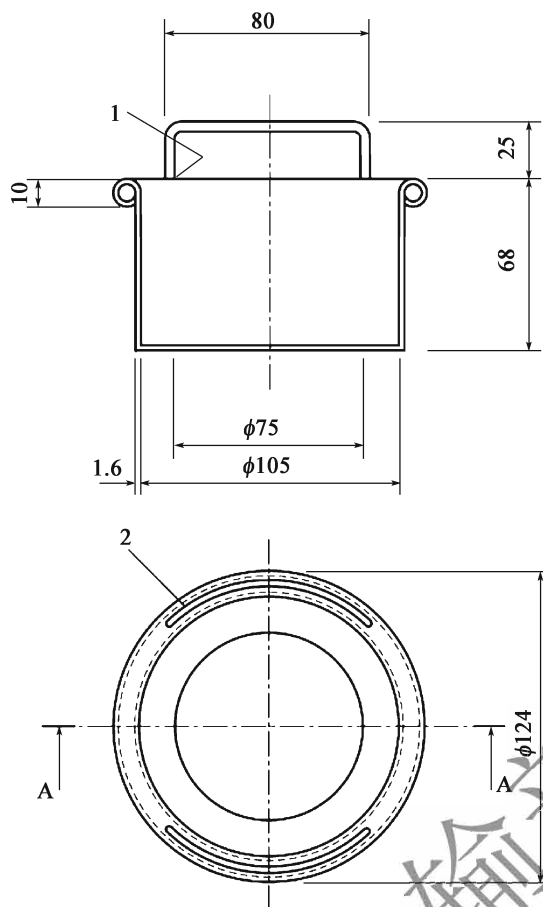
试件盒示意图 (尺寸单位: mm)
